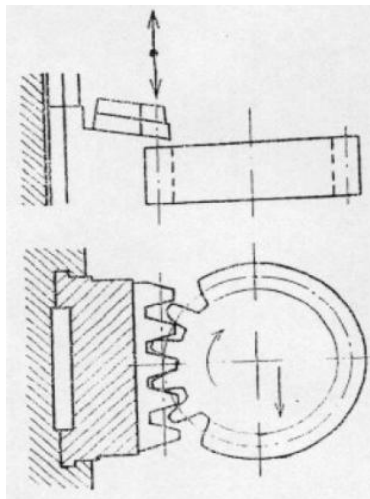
Obrážecí stroj Fellows s parametry [22]
